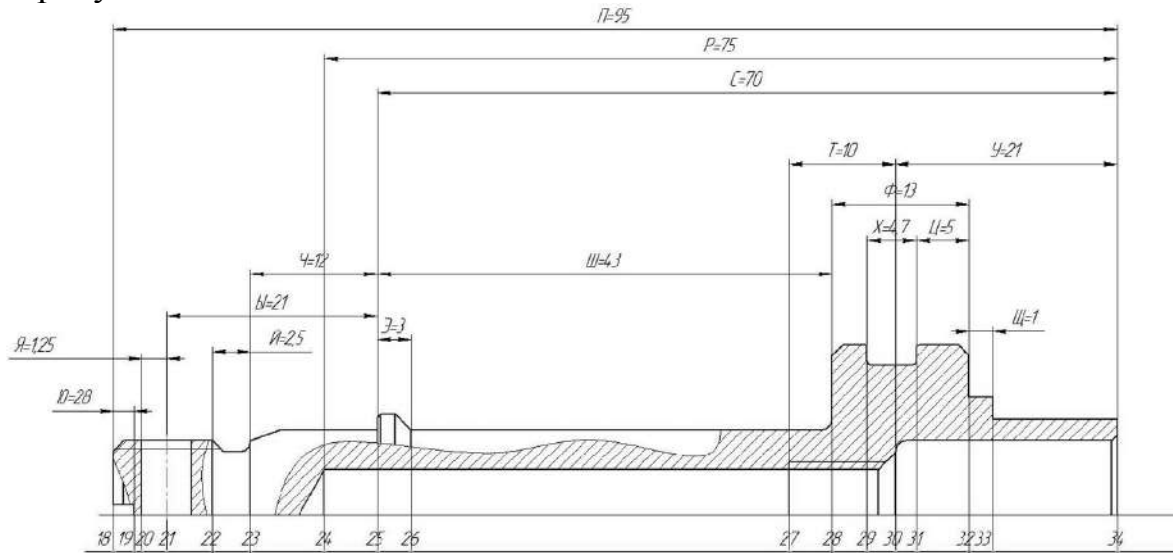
Преобразованный чертёж детали в первой проекции
